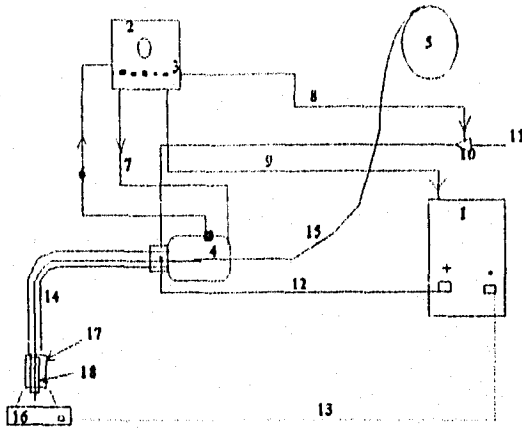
Componentes asociados a un sistema de soldado de bisagras Miller.
